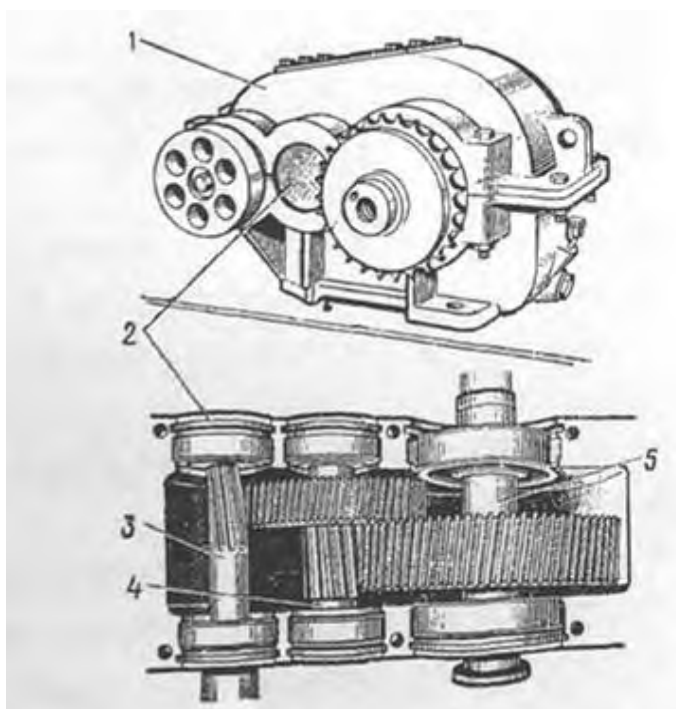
Двухступенчатый редуктор: 1 – крышка редуктора; 2 – подшипниковые узлы; 3 – входной вал; 4 – промежуточный вал; 5 – выходной вал
